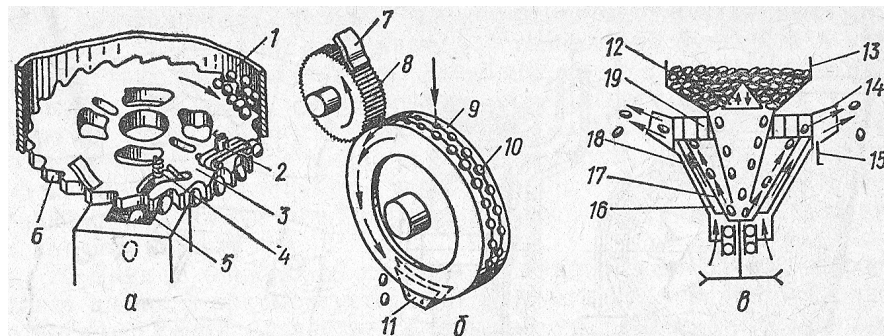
Комірково-дискові (а і б) і відцентровий (в) висівні апарати: 1 і 13 – бункери; 2 – відбивач; 3 – диск; 4 – виштовхувач; 5 – вікно; 6 – комірки диска; 7 – чистик; 8 – ролик; 9 – барабан; 10 – комірки барабана; 11 – клиноподібний виштовхувач; 12 – дозатор; 14 – приймач насіння; 15 – заслінка; 16 – лопатки; 17 – ротор; 18 – корпус; 19 – розподільна головка
